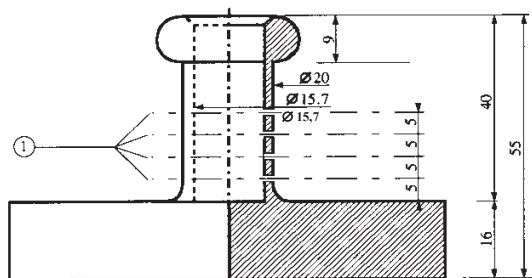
Полый бронзовый цилиндр, закрытый с одной стороны; чертеж и размеры детали в мм
